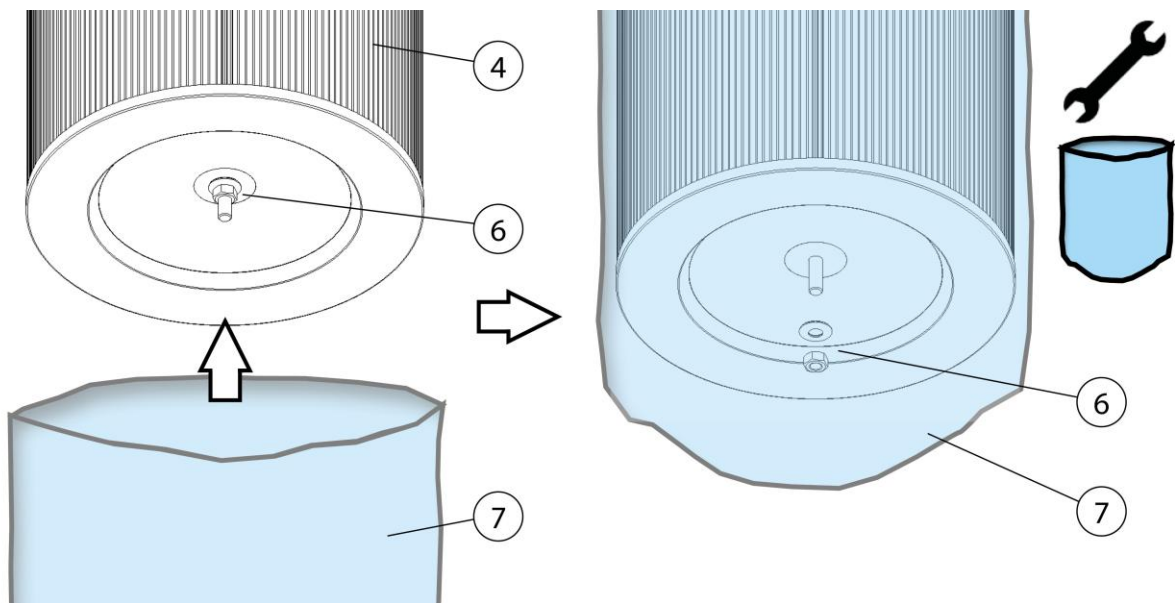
Remplacement du filtre - démontage de la cartouche filtrante
